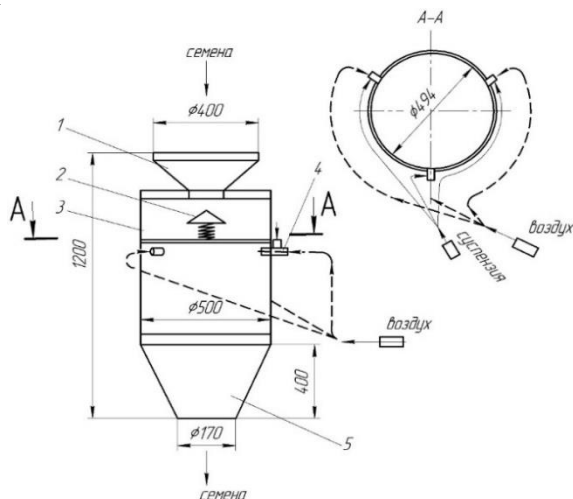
Схема цилиндрической мешалки для семян с форсунками: 1–бункер; 2–разбрызгиватель семян; 3–цилиндрическая мешалка; 4–форсунка; 5–комфюзор
